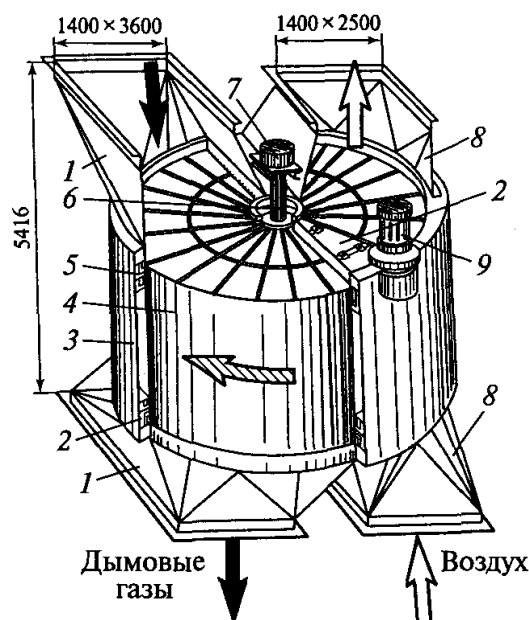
Регенеративный воздухоподогреватель с вращающейся насадкой:
